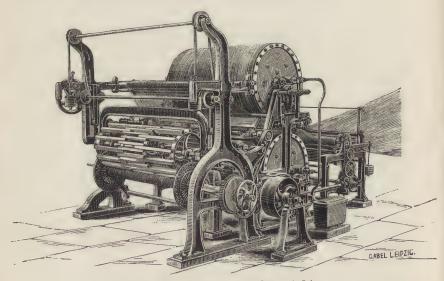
Rettenichlichtmaschine für Jute und Leinen.
